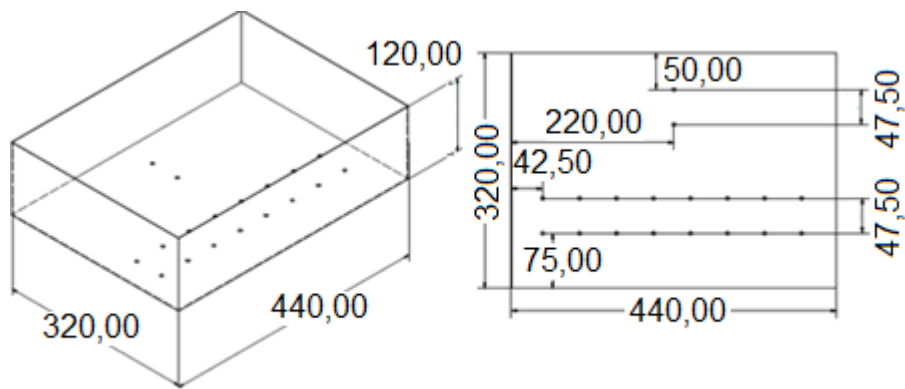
Dimensiones de la caja del tablero de distribución.
